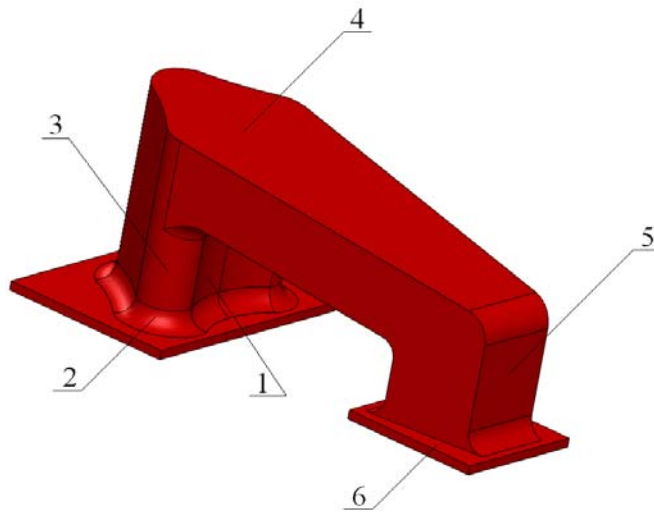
Вузол для закріплення гака ланцюгової стяжки
